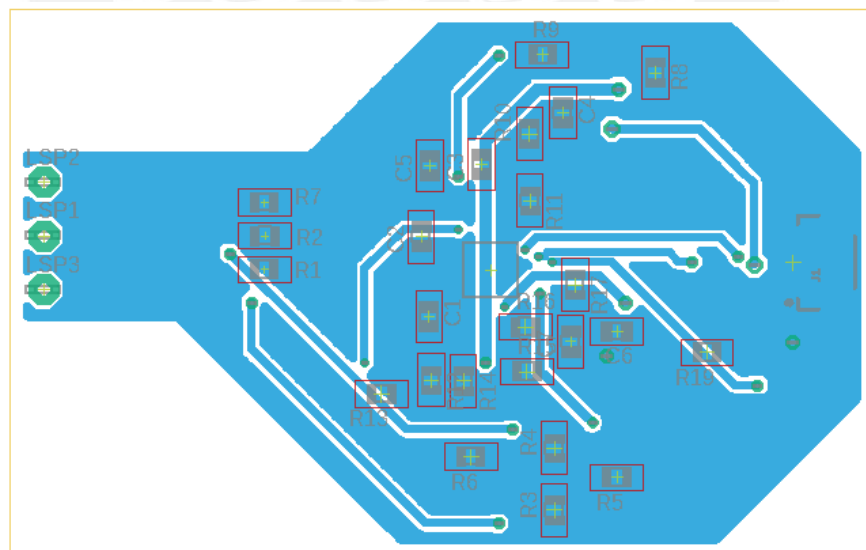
Vista de la base de la tarjeta PCB del bloque ECG
